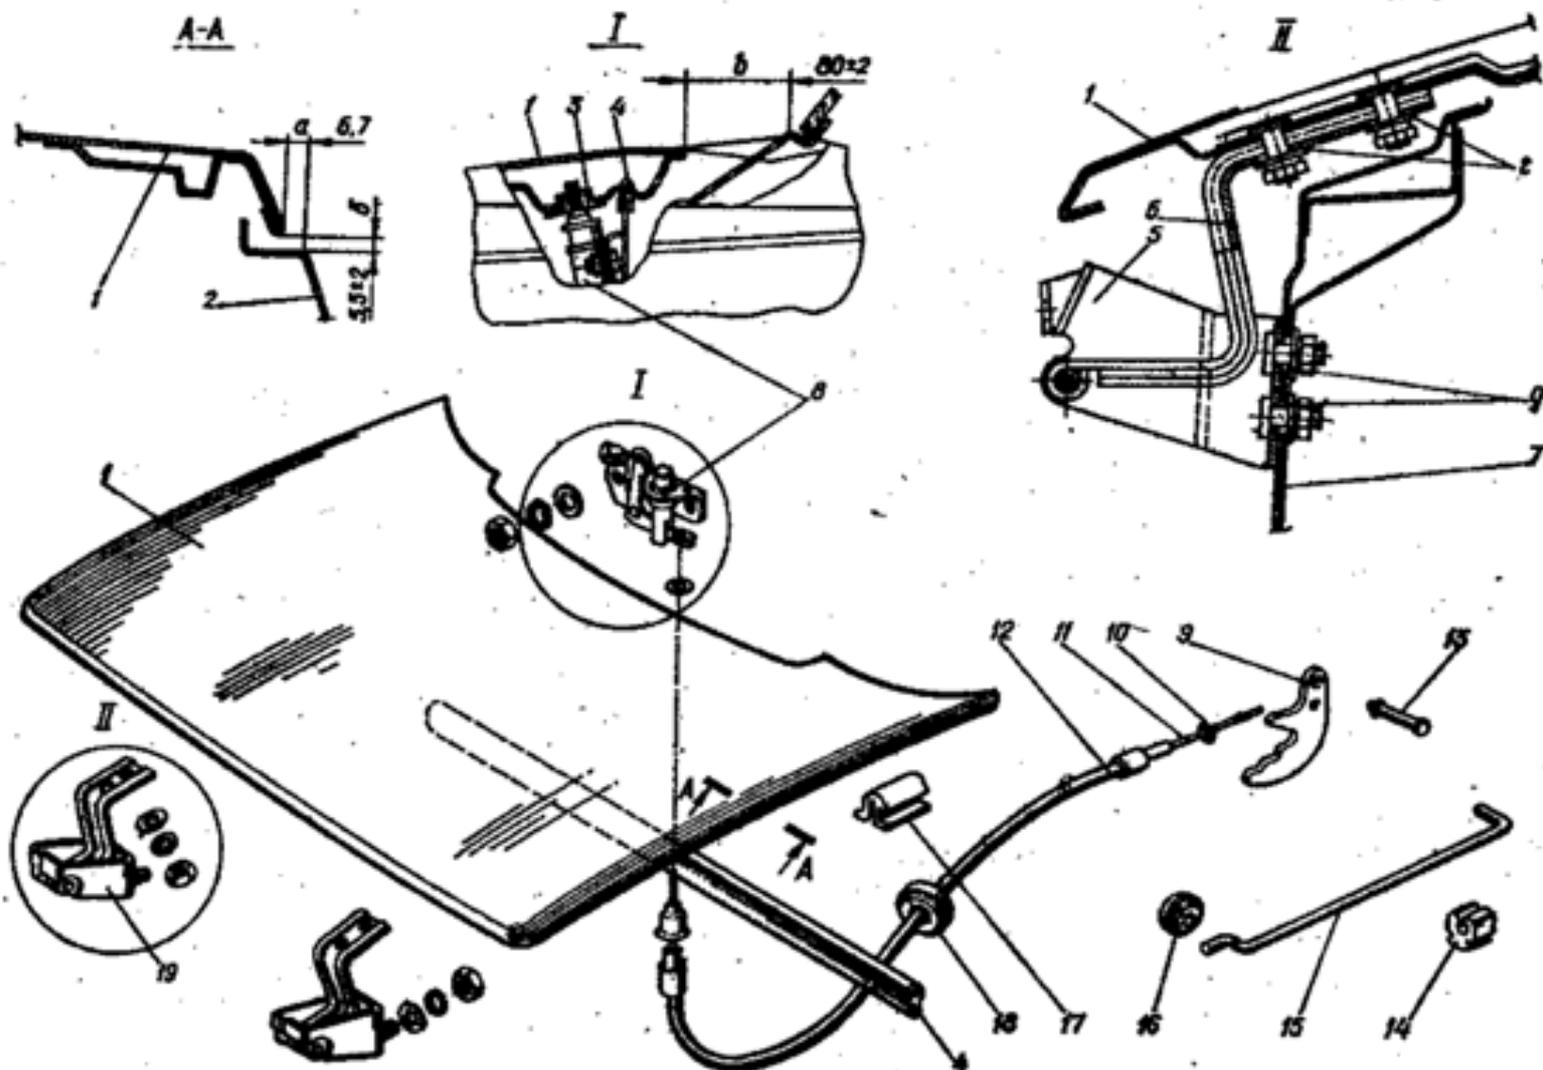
Капот, петли, замок с приводом и установка капота: 1 - капот; 2 - крыло переднее; 3 - фиксатор; 4 - уплотнитель задний; 5 - кронштейн петли; 6 - петля; 7 - панель облицовки радиатора; 8 - замок капота в сборе; 9 - ручка привода; 10 - шайба крепления тяги; 11 - тяга; 12 - оболочка; 13 - ось; 14 - держатель; 15 - упор капота; 16 - втулка; 17 - фиксатор капота; 18 - втулка уплотнительная; 19 - петля в сборе; а - зазор по ширине между капотом и крылом; б - зазор по высоте между капотом и крылом; в - зазор между задней частью капота и нижней частью проема ветрового стекла; г - зазор в отверстиях крепления петель; д - зазор в отверстиях на панели облицовки радиатора.
